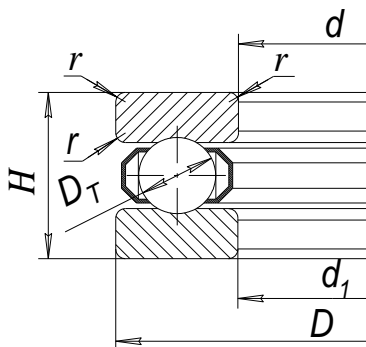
Підшипник кульковий упорний одинарний
